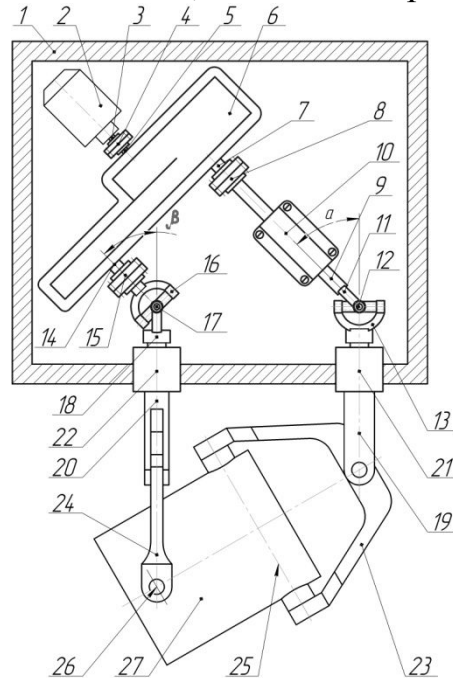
Машина для обробки деталей, в конструкції якої застосовується привод з двома шарнірами Гука
